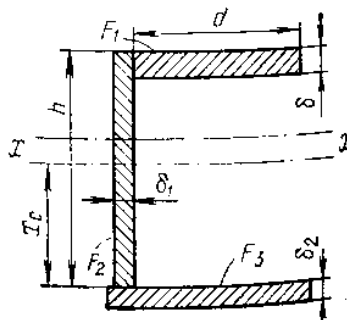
Поперечное сечение опорно-концевой стойки
